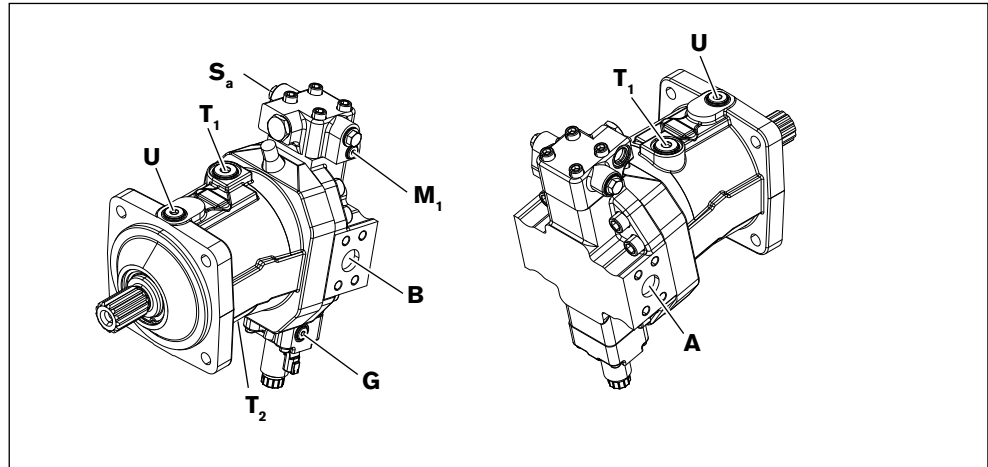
Vue d'ensemble des raccords A6VM avec réglage EP1/EP2 et valve de rinçage, raccords de service sur le côté
